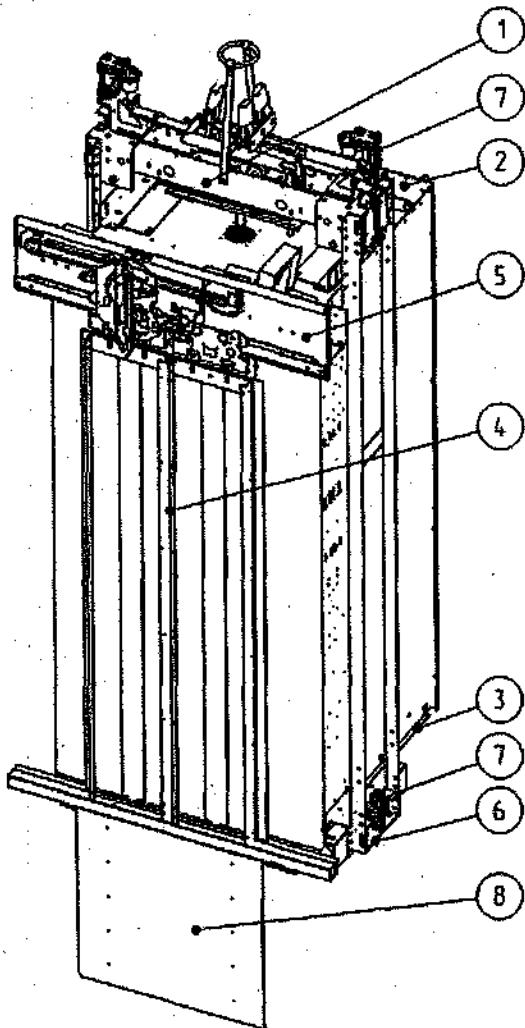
Кабина: 1 – балка верхняя; 2 – потолок; 3 – пол; 4 – створки; 5 – привод дверей кабины; 6 – балка нижняя; 7 – башмак скользящий; 8 – фартук.
